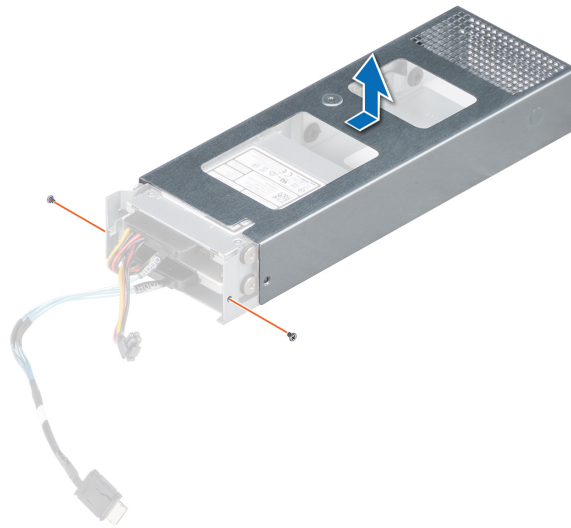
Entfernen der Abdeckung für das 2,5-Zoll-Laufwerksgehäuse
